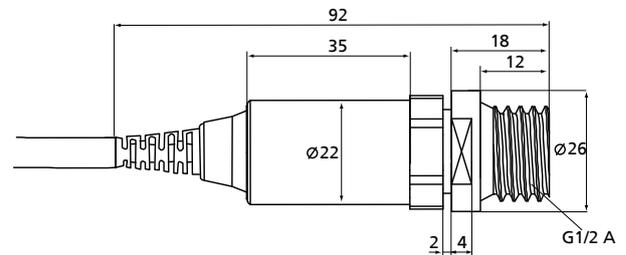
Dimensões do sensor na faixa de medição a partir de 65 bar
